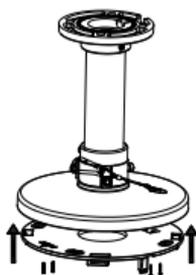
Установка адаптерной пластины на подвесной кожух
